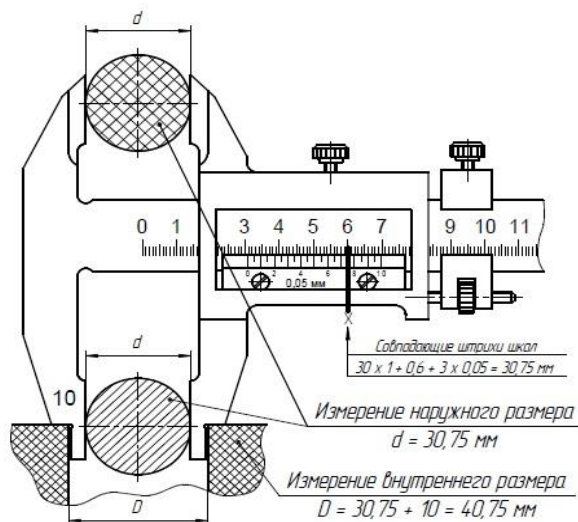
Измерение размеров деталей штангенциркулем типа II
